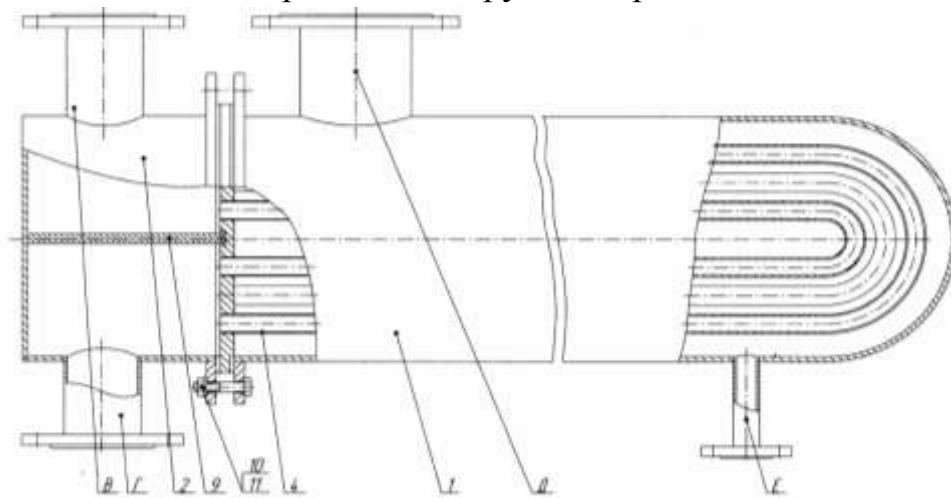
Теплообмінник з U- подібними трубами: 1 - кожух; 2 – продуктова камера; 4 – трубка; 9 – перегородка; 10,11-болтове з'єднання
